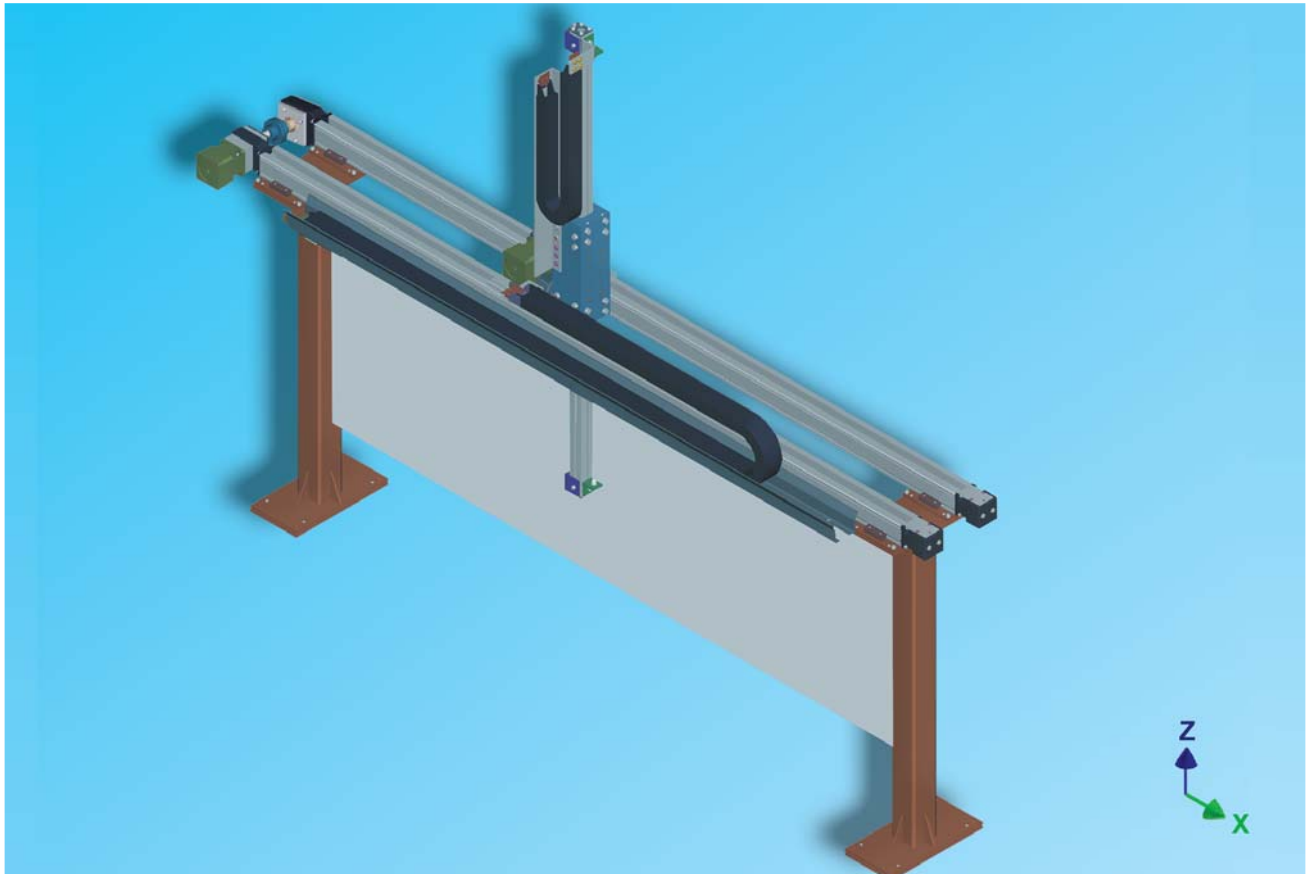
zeigt Ausführung mit Stahlunterbau (optional)
